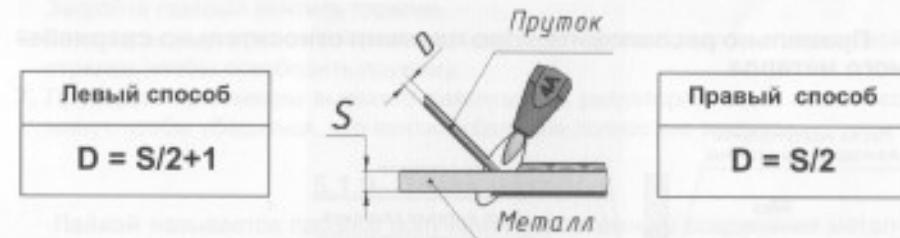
Выбор диаметра сварочной проволоки (прутика).
